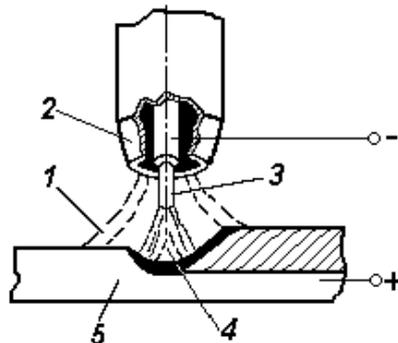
Схема дуговой сварки в атмосфере защитного газа
